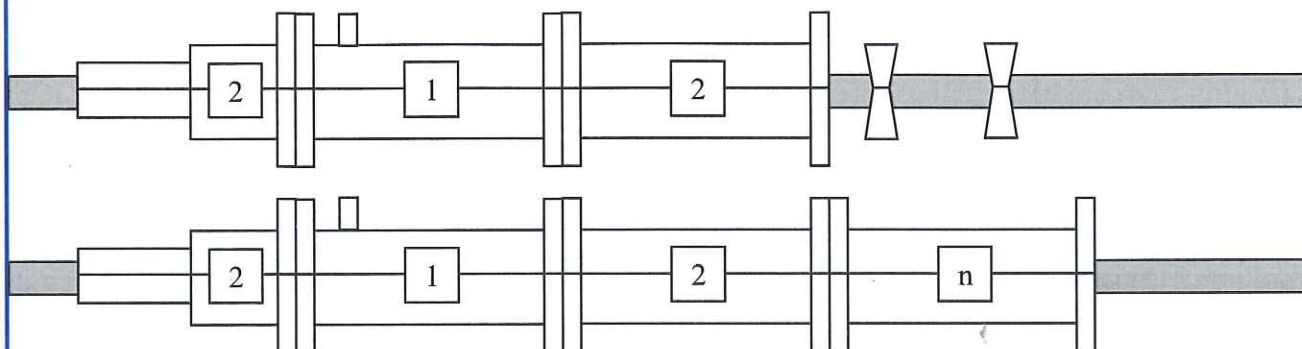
Сборка по вертикальным фланцам секций FT-Tube и FT-End
